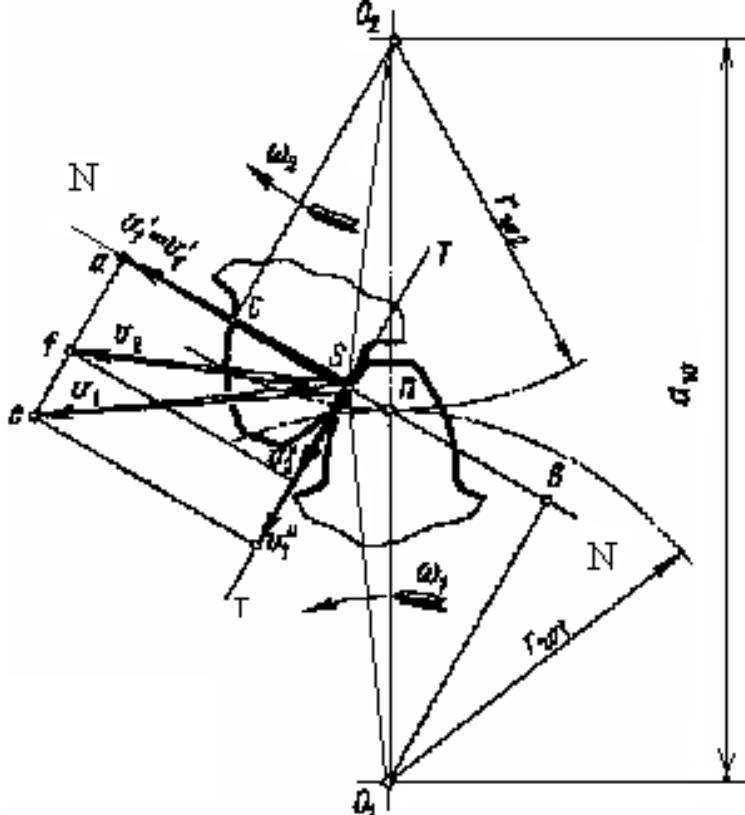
Схема зацепления пары зубчатых колес
